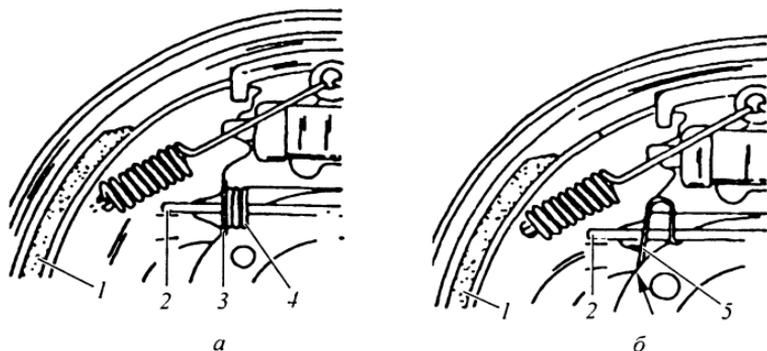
Расположение пружин на нажимной планке для установочных механизмов различных фирм: а — Mercedes-Benz; б — Perrot; 1 — передняя тормозная колодка; 2 — нажимная планка; 3 — опора пружины; 4 — нажимная пружина; 5 — листовая пружина
